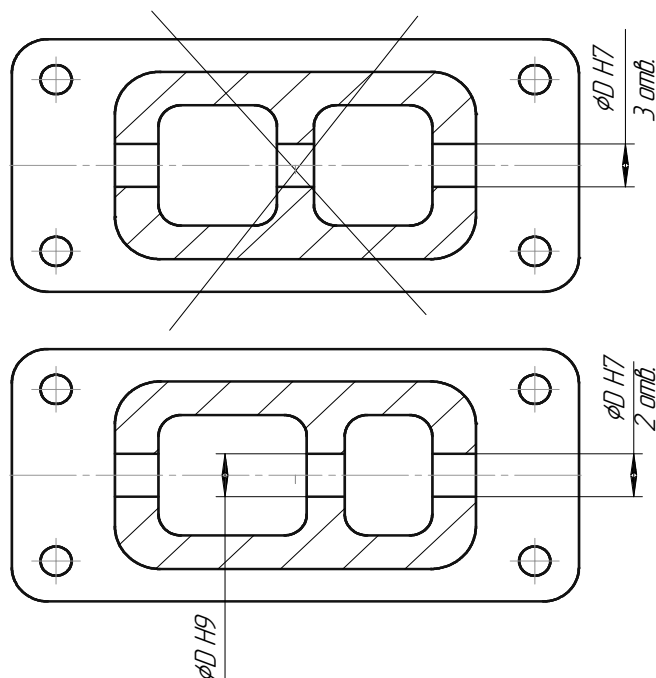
Конструкция технологичной детали по удобству обработки точных отверстий
